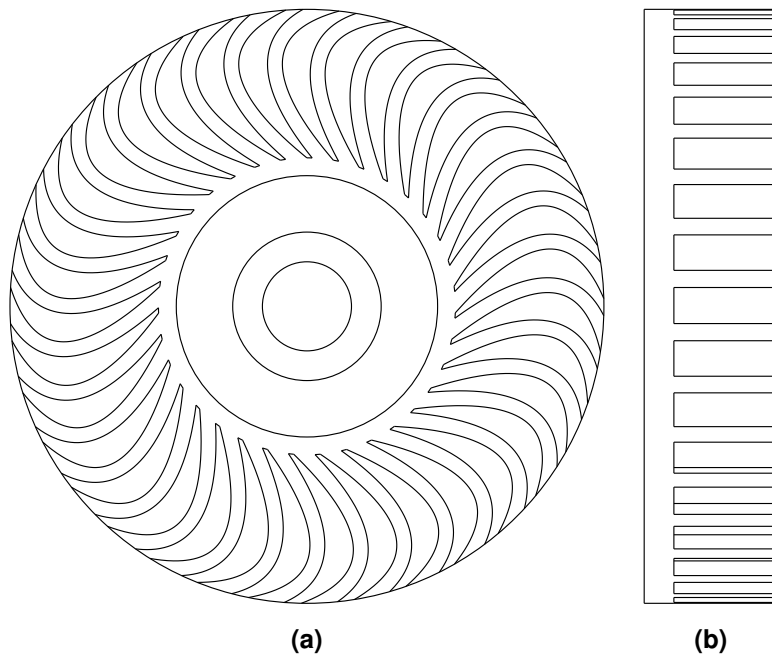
Zeichnung des 3D-gedruckten Rotorelements *3D_B* mit $\varnothing 20$ mm, 35 Schaufeln und einer Schaufelhöhe von 3,5 mm. (a): Draufsicht; (b): Seitenansicht.
